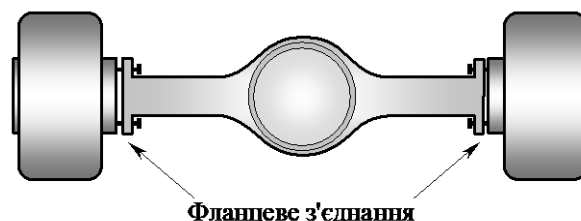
Схема з'єднання корпусу моста з бортовими редукторами
